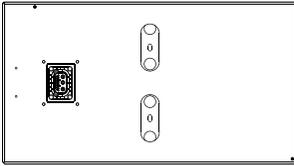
(1) Dehnschrauben zur Befestigung des Bodendeckels
